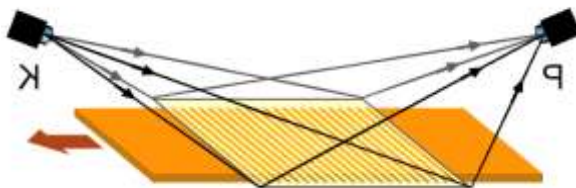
Схема прибора для проверки плоскостности поверхности и измерения ширины
